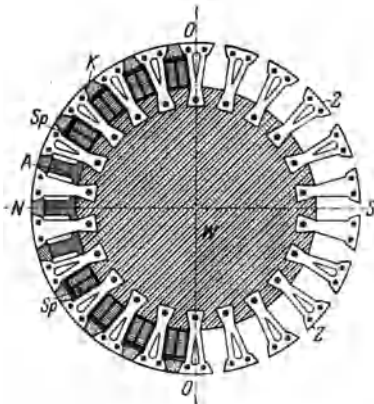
Feldmagnet für Turbodynamos mit eingesetzten Blechzähnen.
